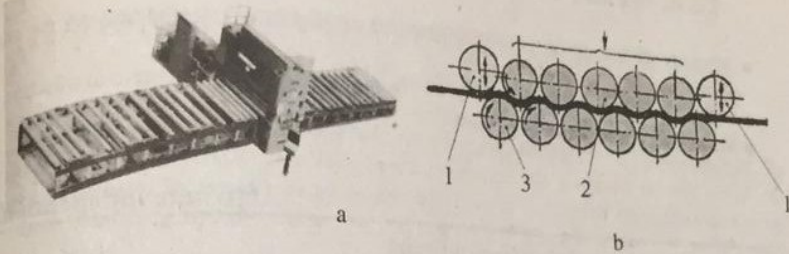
Mașină pentru îndreptat tablă cu cilindri: a - vedere; b - schemă.
